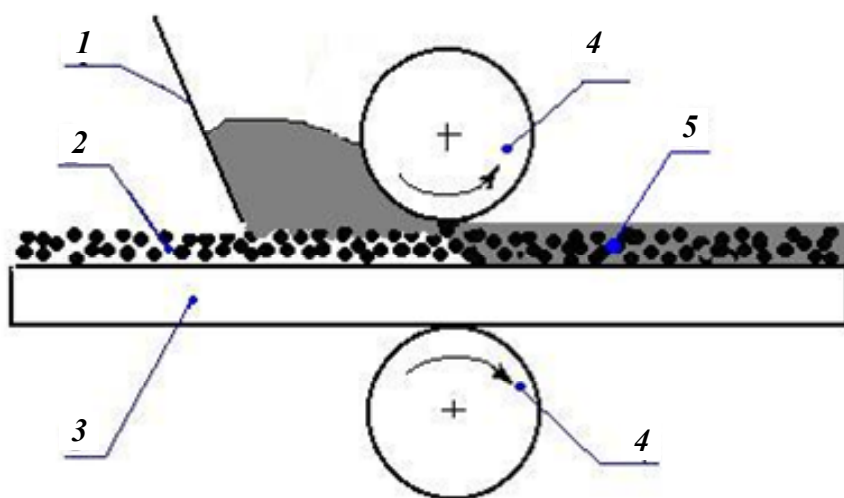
Схема пропитки бронзового слоя пастой фторопласта: 1 – бункер с пастой; 2 – пористый бронзовый слой; 3 – стальная основа; 4 – прокатные валки; 5 – пористый слой, пропитанный фторопластом
